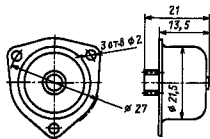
Габаритные и установочные размеры двигателя ДШ21-0,00005-22,5
